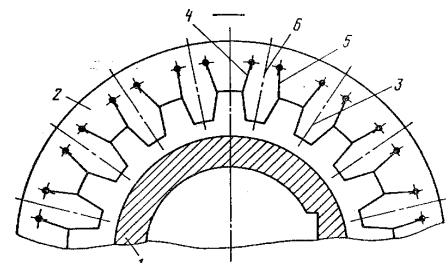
Упругая обойма с прорезями с обеих сторон зубьев
